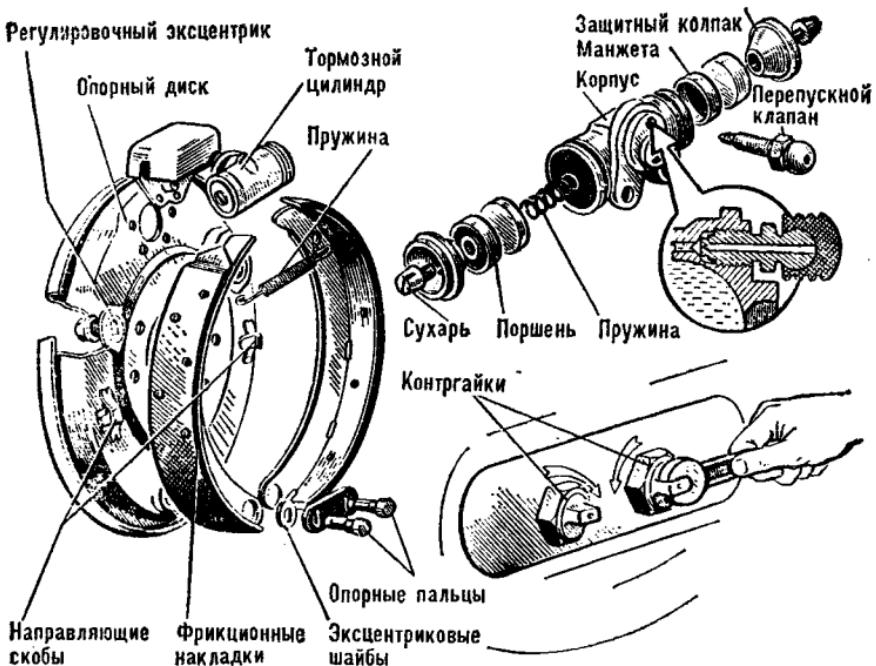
Колесный тормозной механизм барабанного типа с гидравлическим приводом
